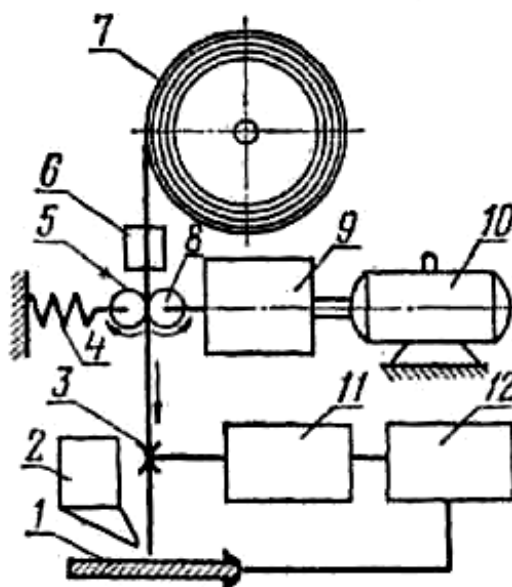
Схема автоматической сварочной головки:
